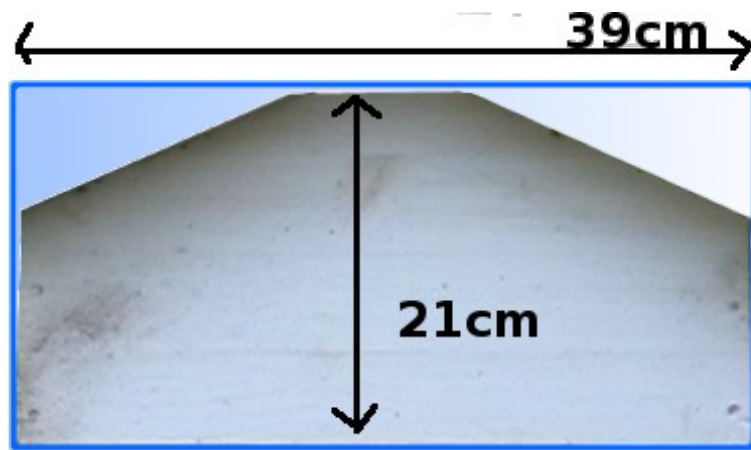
Das Blaue wird weggeschnitten für die Front
